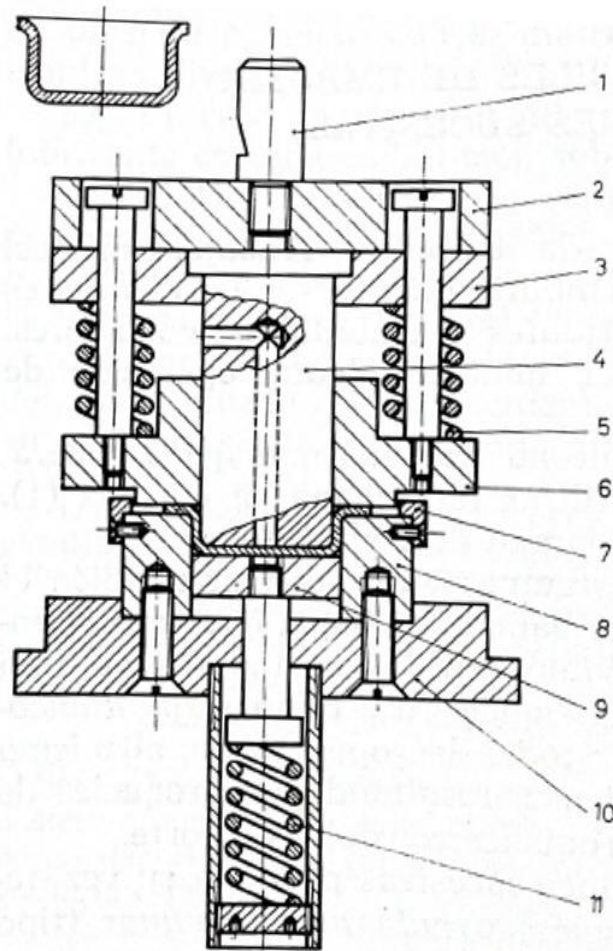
,01. — Estampa de embutición directa con prensachapa. *Parte superior:* 1, mango; 2, contraplaca; 3, placa portapunzones; 4, punzón; 5, muelles; 6, prensachapa. *Parte inferior:* 7, toques de posicionamiento de la chapa; 8, matriz; 9, expulsor; 10, base inferior; 11, muelle de accionamiento del expulsor.
